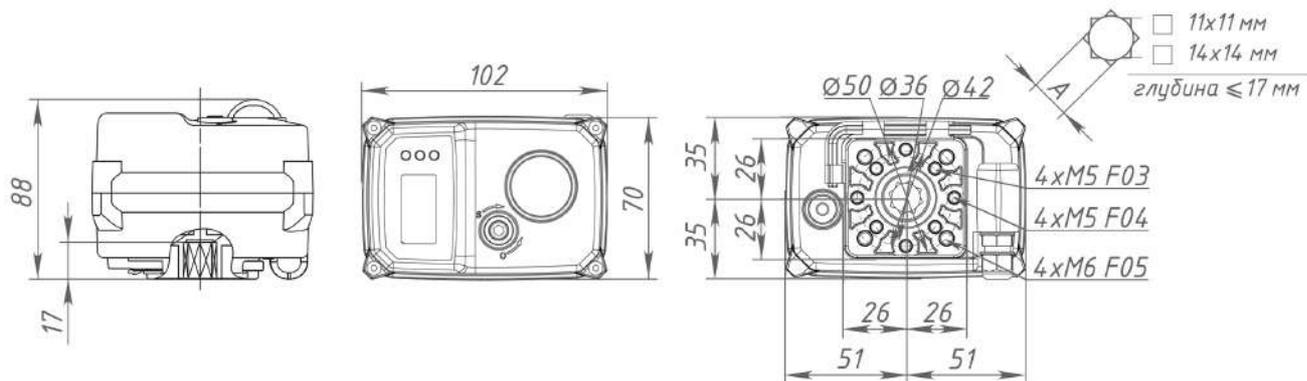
Габаритные размеры электроприводов Motorvalve серии Smart S20.
